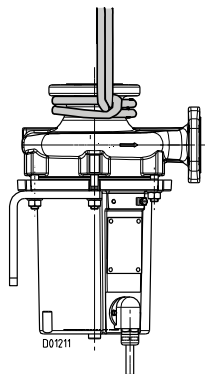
Транспортировка насосного агрегата (вертикально - двигатель вниз)
